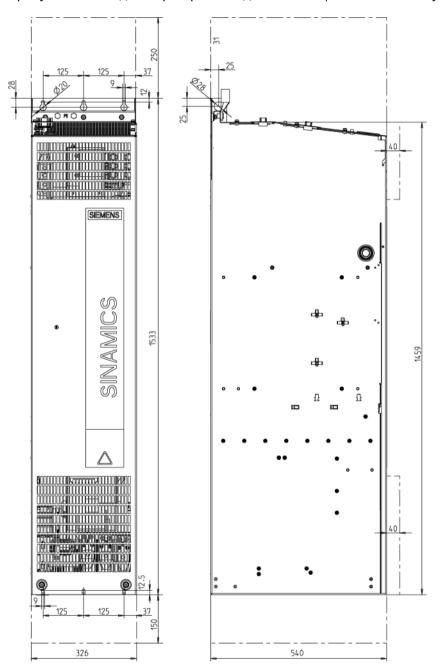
Габаритный чертеж модуля двигателя, типоразмер GX. Вид спереди, вид сбоку
